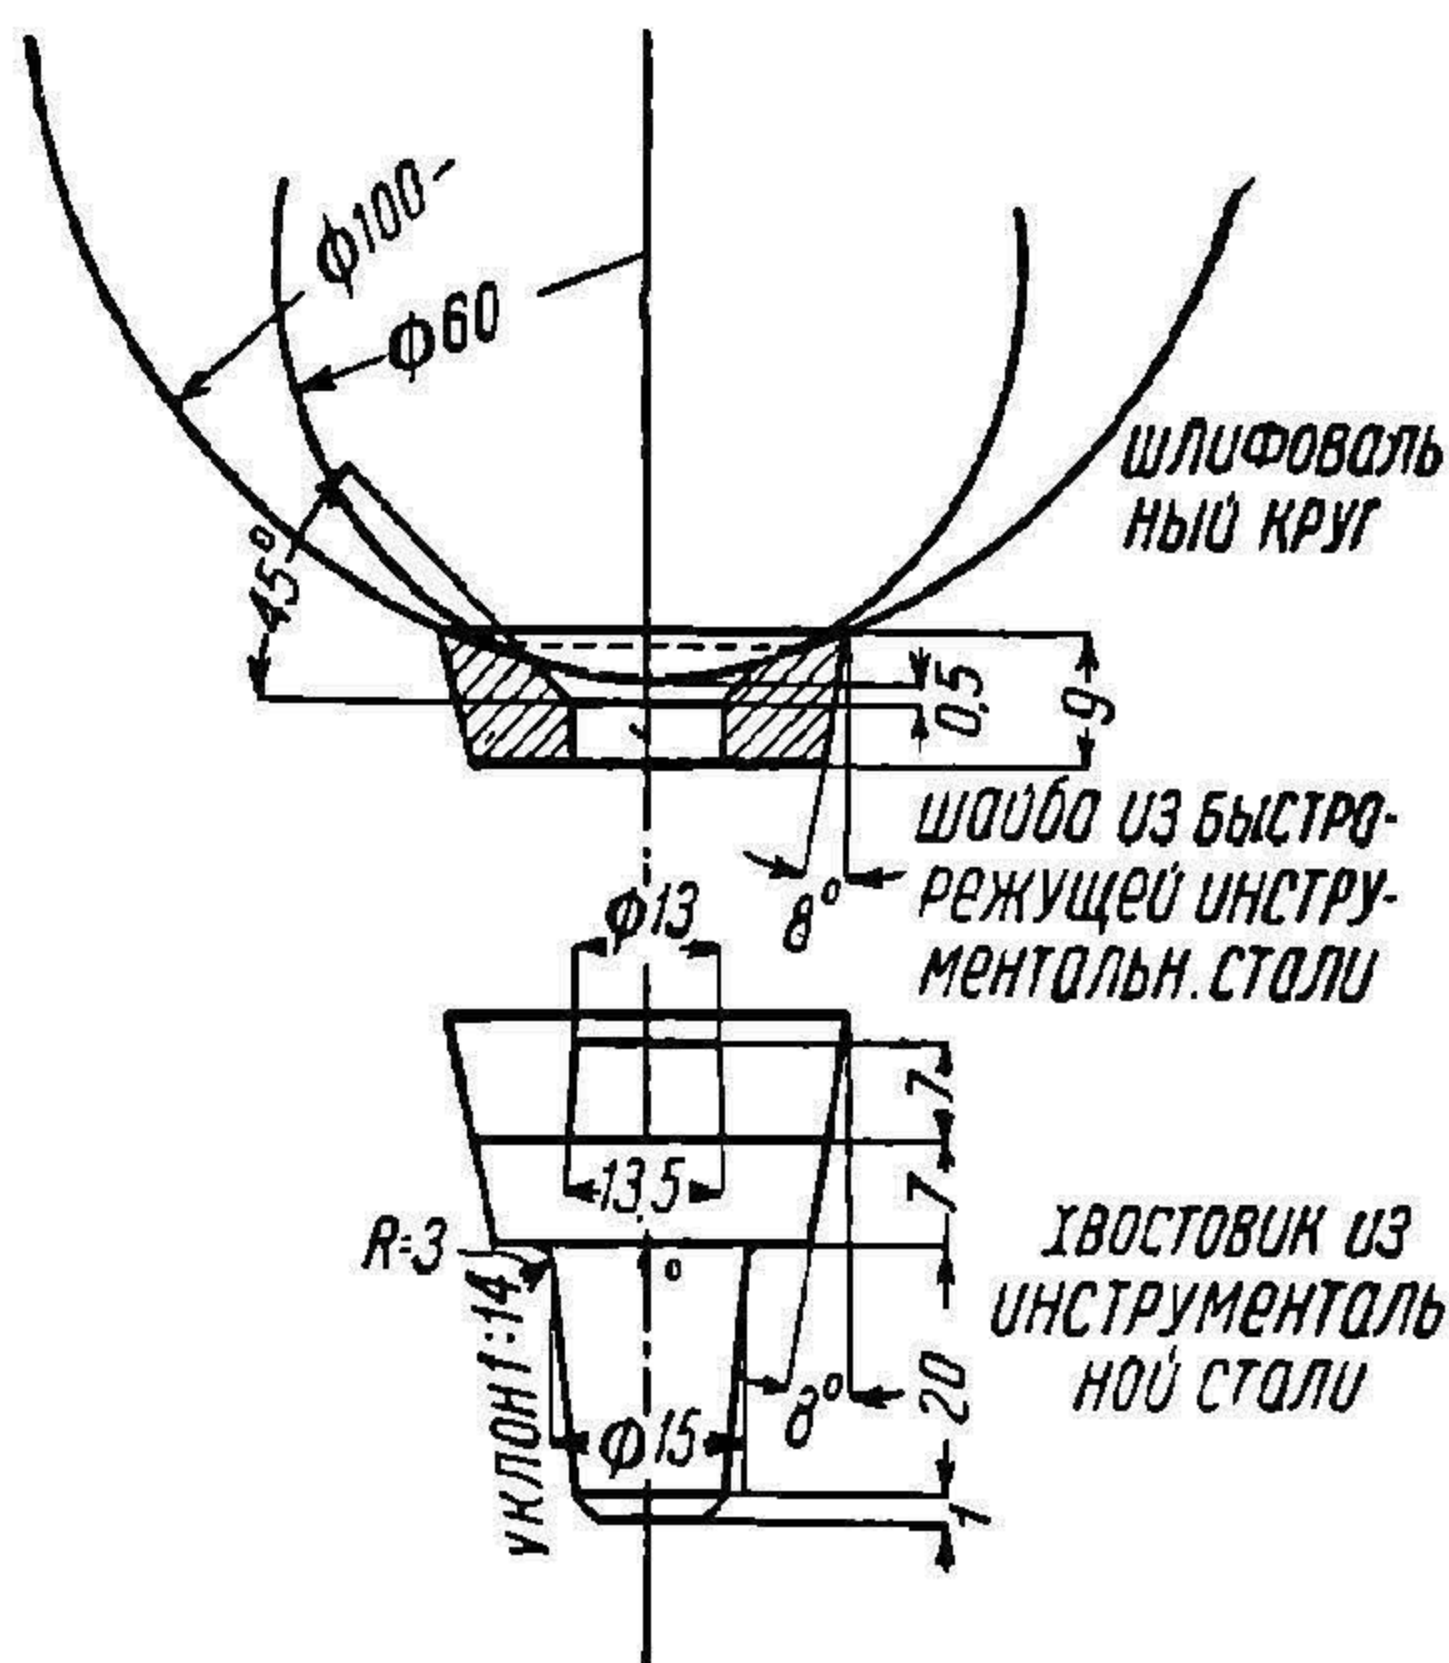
„Грибковый“ или „чашечный“ резец для колесно-токарных работ.
